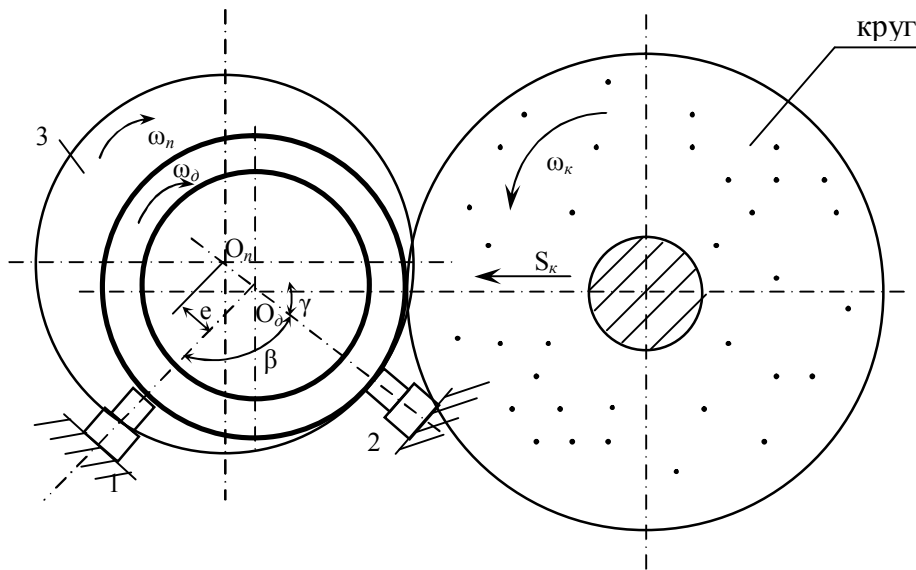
Схема безцентрового круглого шліфування доріжки кочення внутрішнього кільця роликопідшипника
